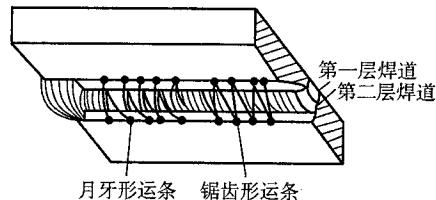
6 V 型坡口对接仰焊的运条方法
